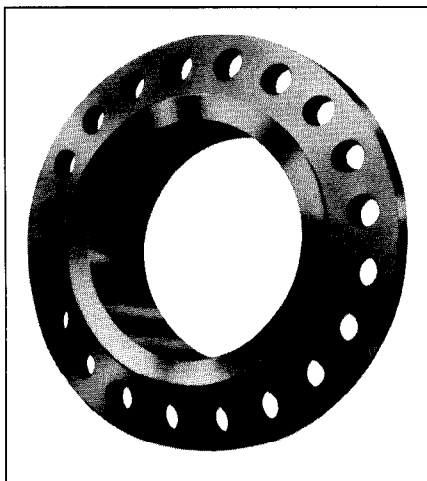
Vorschweißflansch, Werkstoff 10Ni 14, Innendurchmesser 850 mm.
